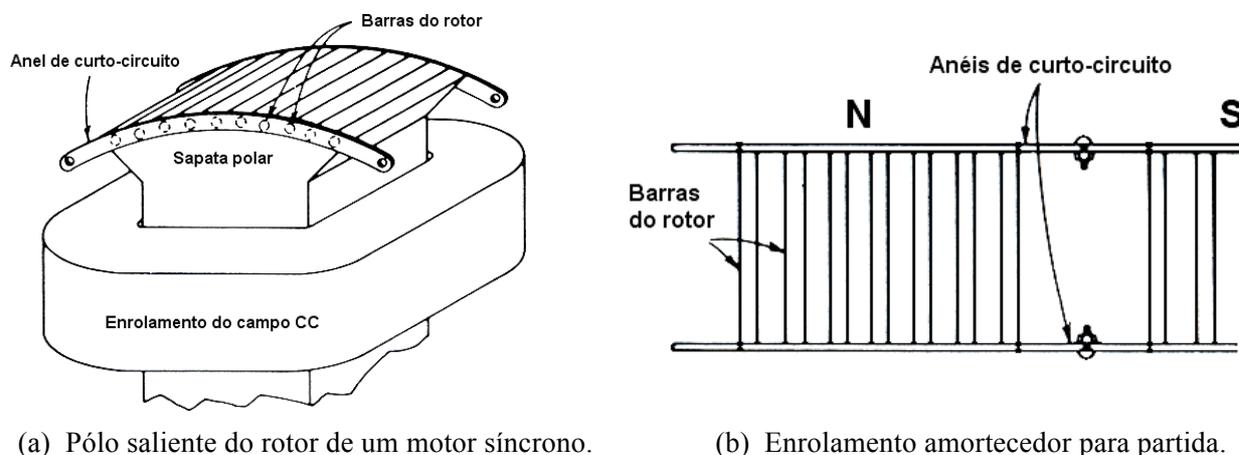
Enrolamento amortecedor de um motor síncrono, para partida como rotor de gaiola.
